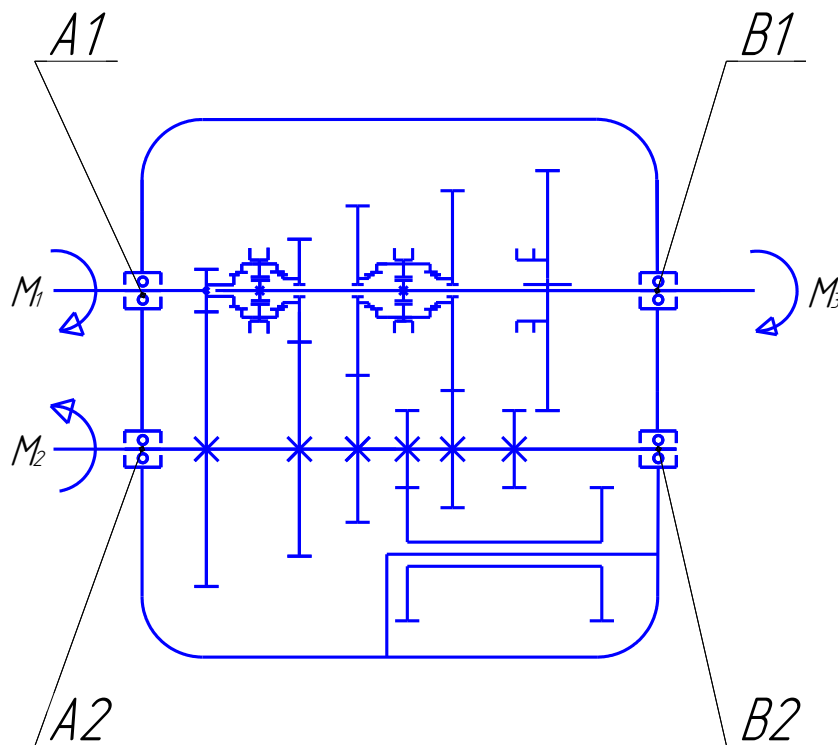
Схема коробки передач ВАЗ 2108 (А1, А2, В1, В2 – підшипники)
